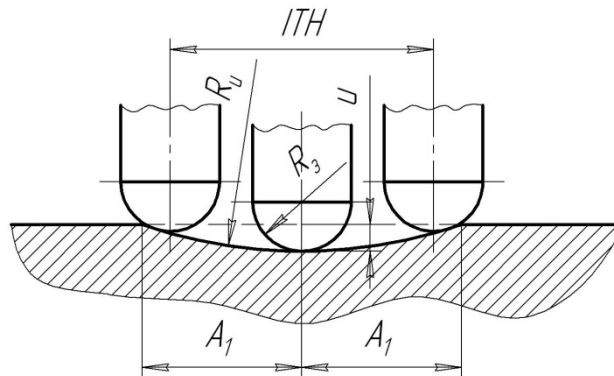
Контакт сферической заготовки с плоской поверхностью установочной опоры
